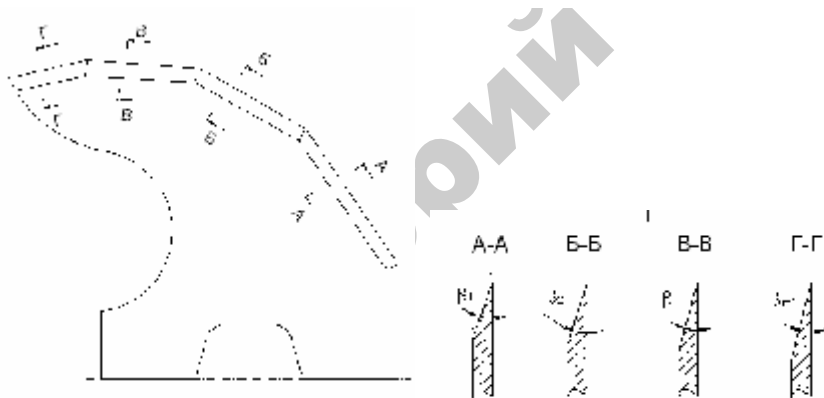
Схема куттерного ножа с изменяющимся углом заточки режущей кромки
